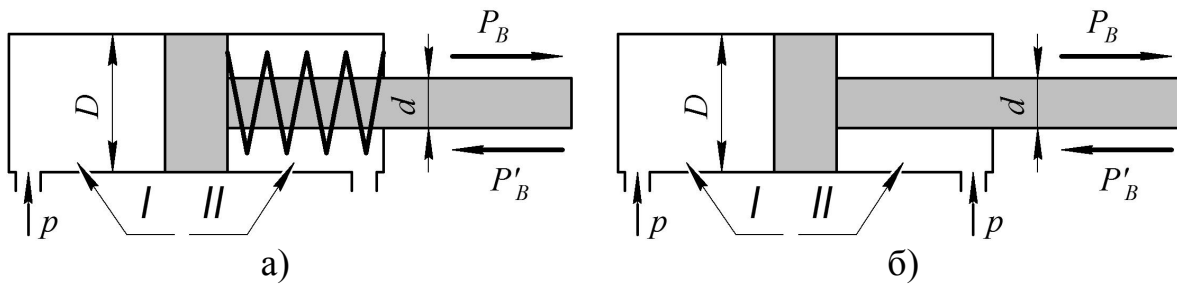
Схеми конструкцій пневмоциліндрів
